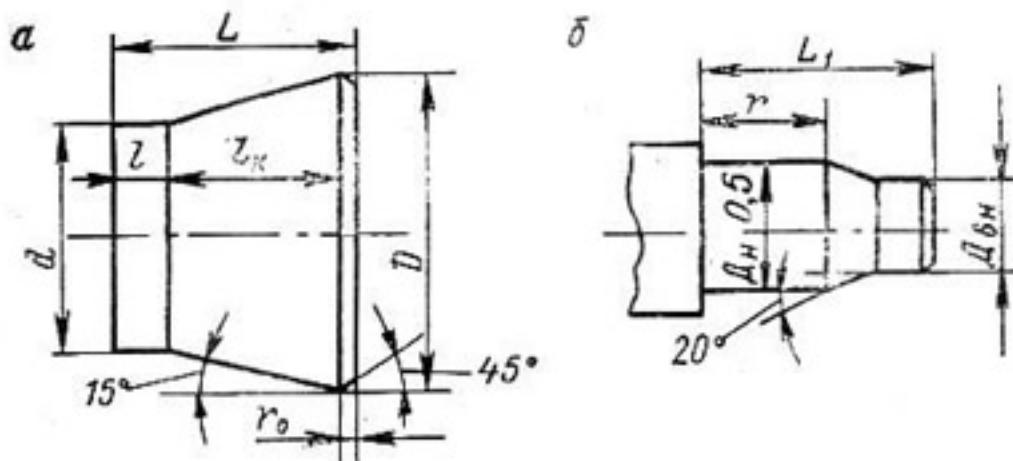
Формовочные оправки длястыковки пластмассовых коллекторных труб:
